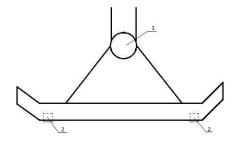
Управляемая стопа шагающего робота: 1 — реверсивный двигатель, 2 — датчик касания
